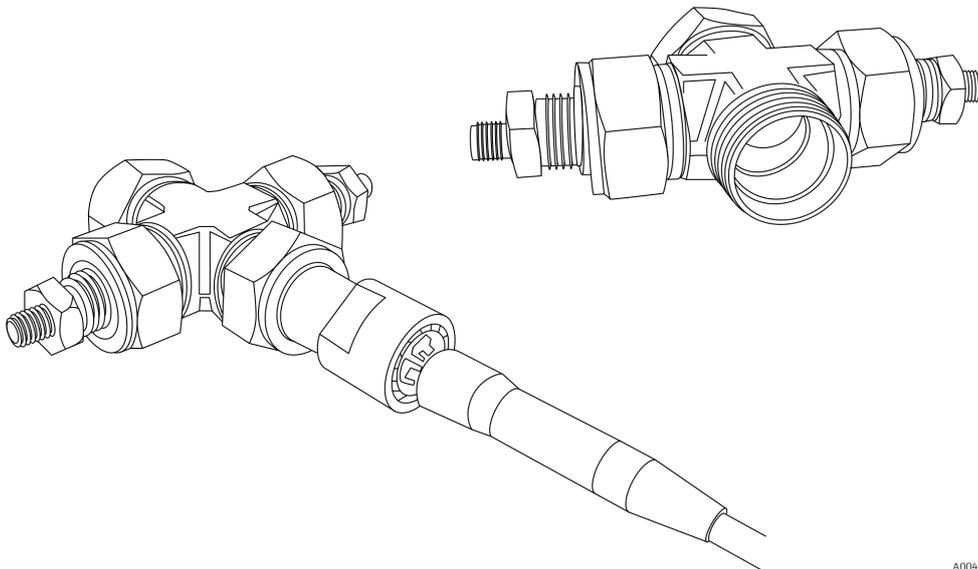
Rxn-30-Sonde in 1in-Kreuzanschlussstück mit Standardklemmverschraubung eingesteckt
